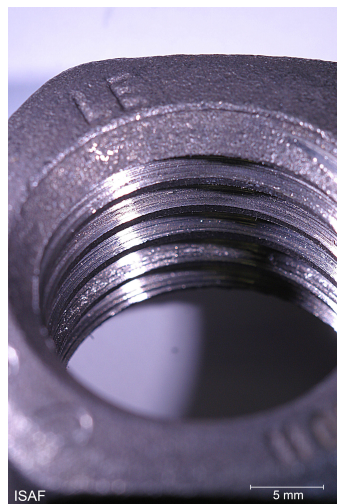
Gewindeprüfkörper axial belastet mit 60kN (Mutter)
